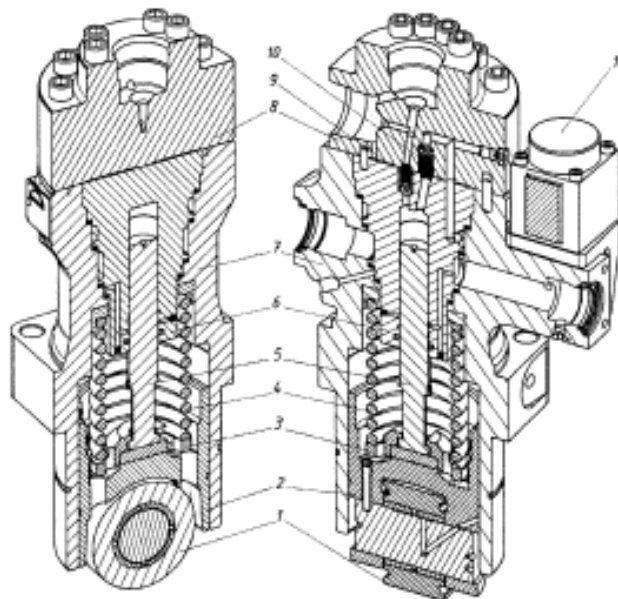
Паливний насос високого тиску серії фірми MAN: 1 - ролик штовхача; 2 - штовхач; 3 - нижня тарілка поворотної пружини; 4 - поворотна пружина; 5 - плунжер; 6 - втулка плунжера; 7 - корпус; 8 - кришка; 9 - нагнітальний клапан; 10 - наповнювальний клапан; 11 - дросельний клапан керування подачею з електромагнітним приводом
